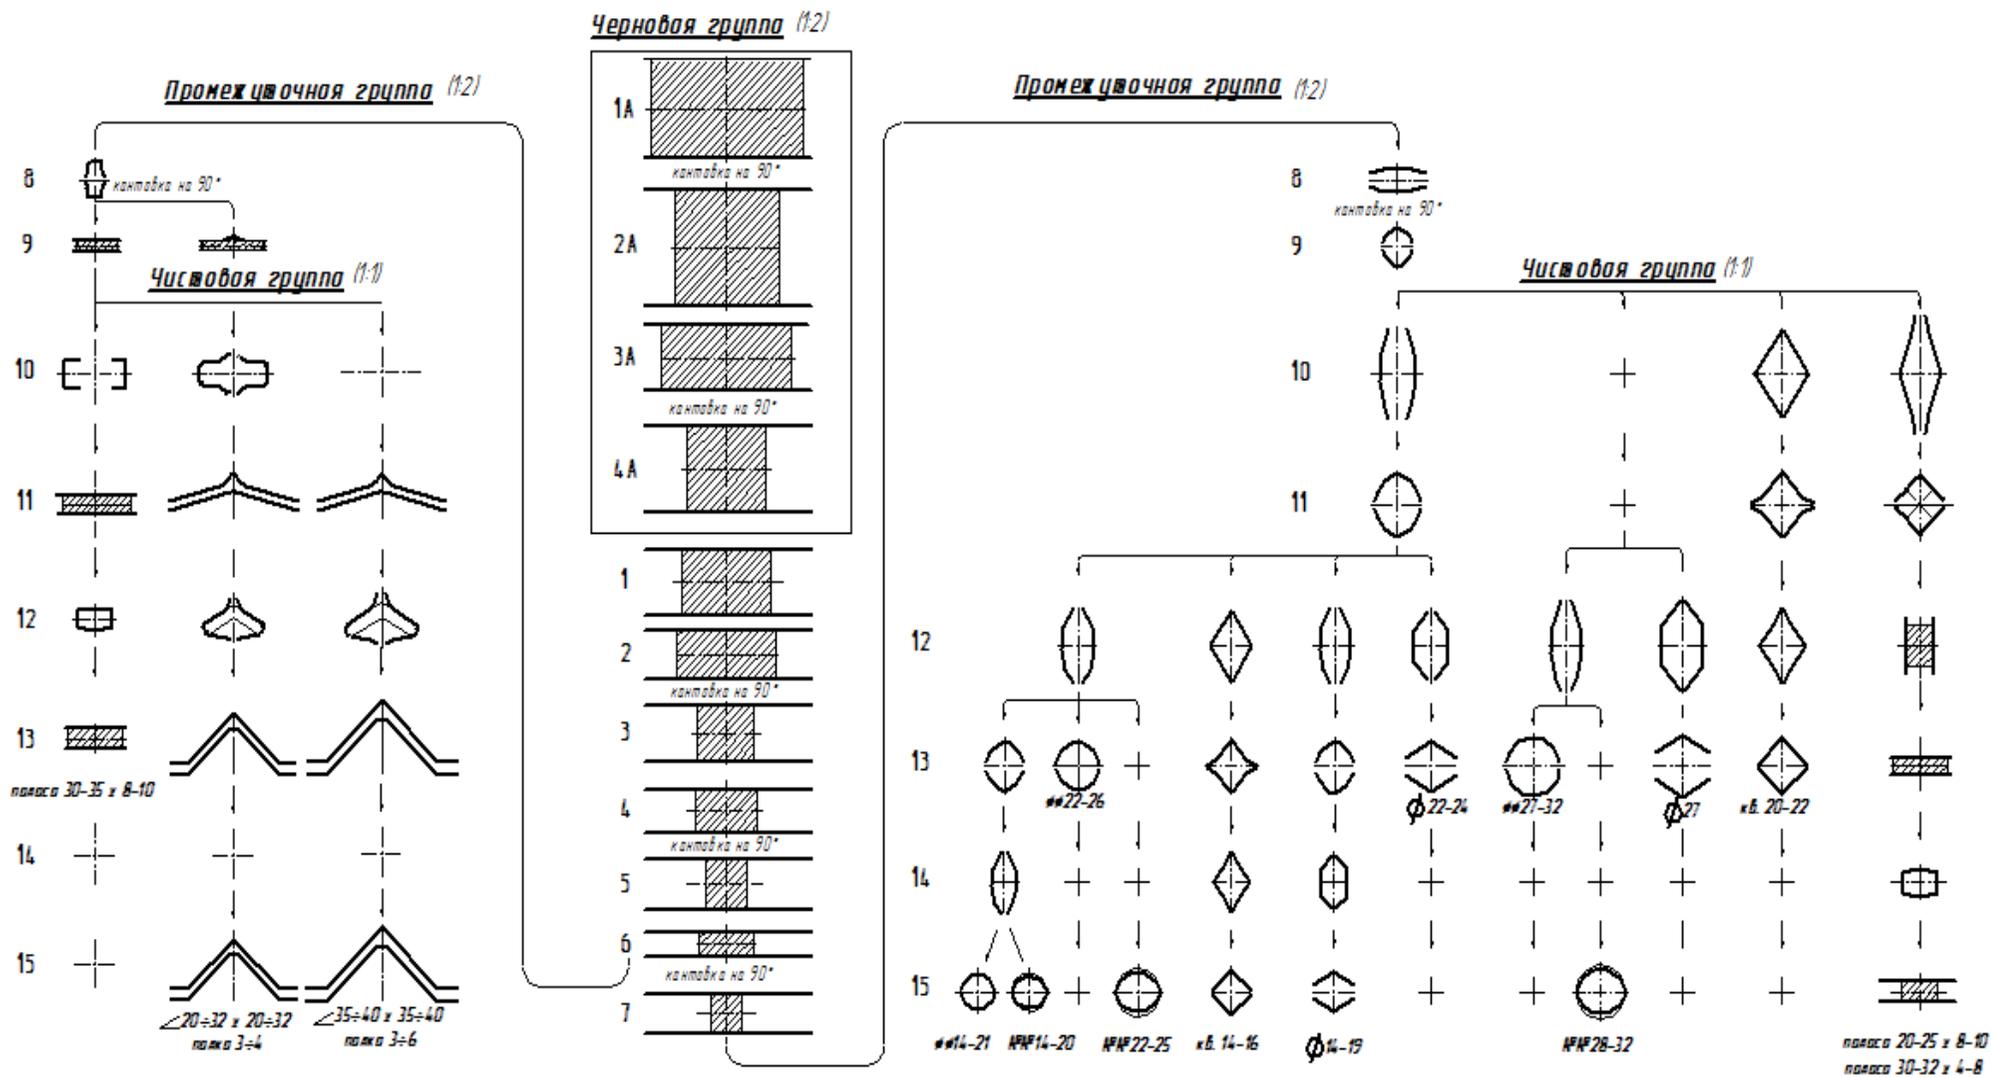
Возможные схемы калибровок валков мелкосортного стана 250 с применением бескалибровой прокатки и после реконструкции черновой группы клетей
